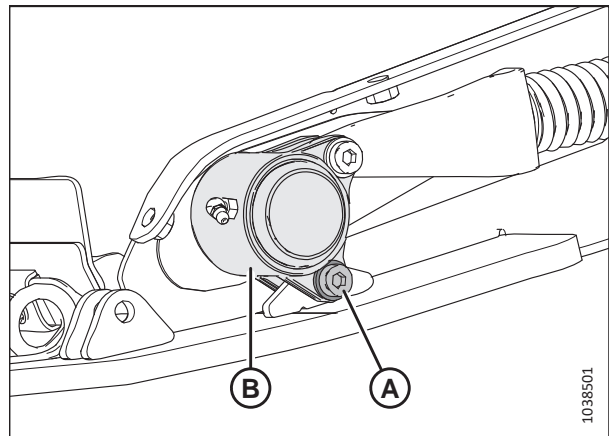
Pieza de fundición del rodamiento del rodillo tensor:
